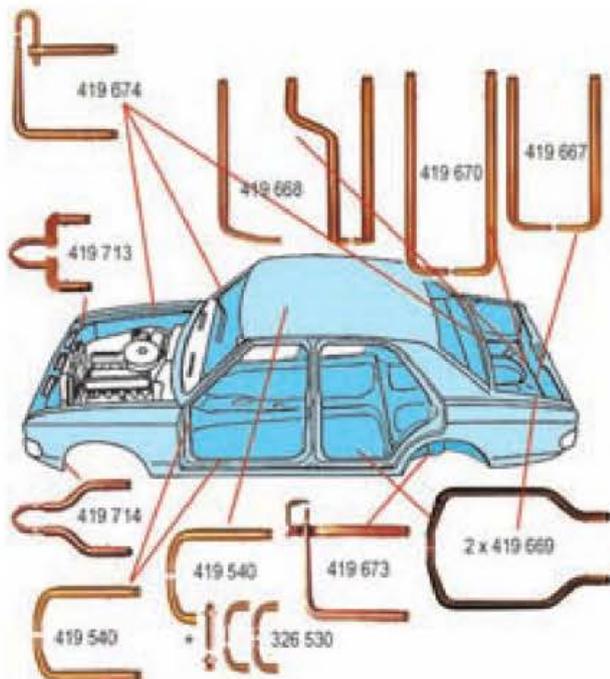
Diferentes electrodos para soldadura por resistencia.
